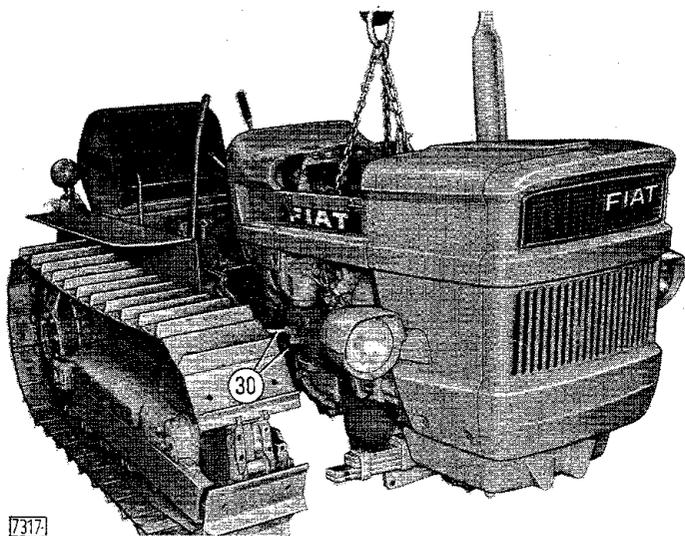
Stacco (riattacco) del gruppo motore-cambio mediante la catena di sollevamento 290740.
